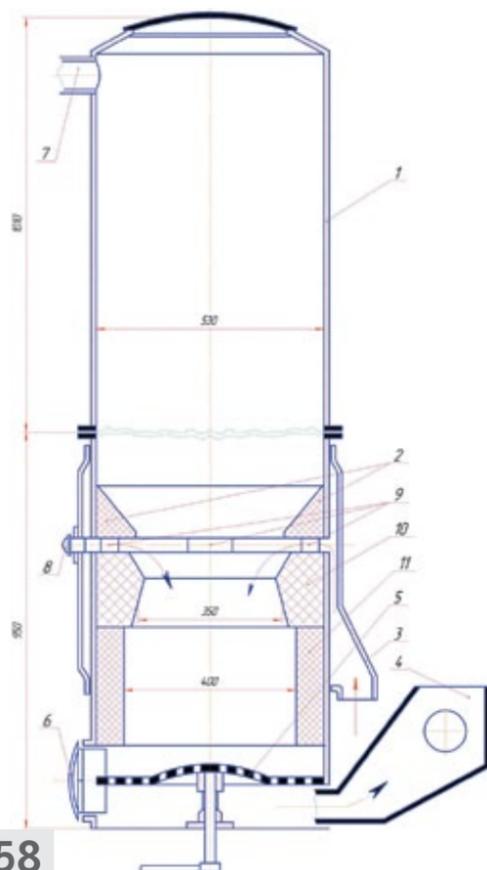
Газогенератор Abogen (Германия): 1 – бункер; 2, 10, 11 – вкладыши; 3 – воздухоподающий патрубок; 4 – газосборник; 5 – колосниковая решетка; 6 – люк зольника; 7 – паропроводный патрубок; 8 – люк; 9 – фурменные отверстия
